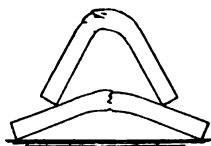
Biegeprobe bei autogen geschweißten Stäben.
